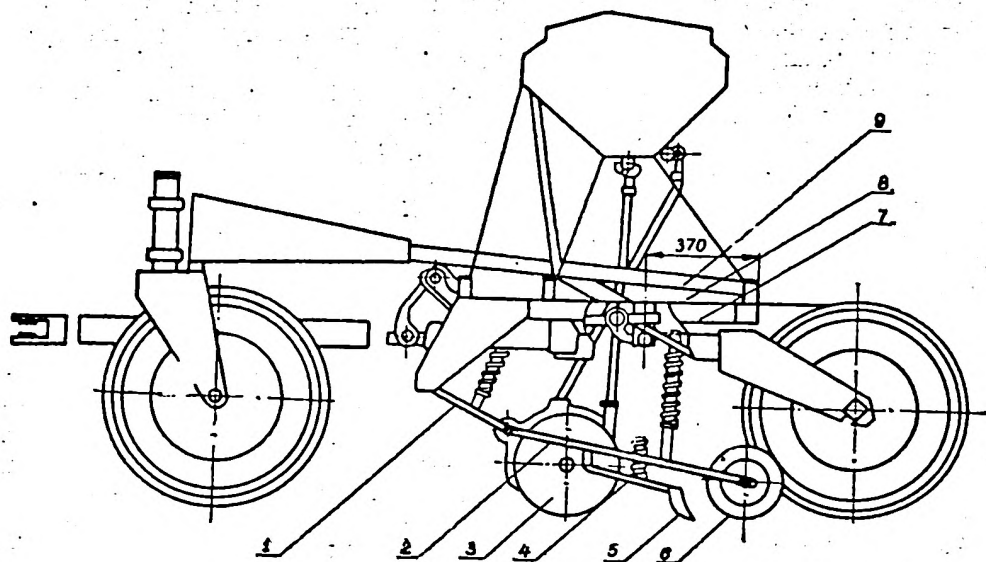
Схема переоборудования сеялки с комбинированными двухдисковыми сошниками и прикатывающими катками
